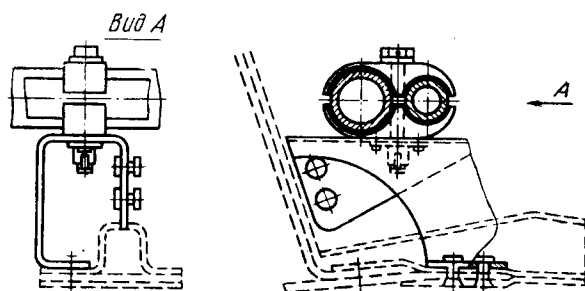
Крепление колодок к элементу конструкции на анкерных гайках.
